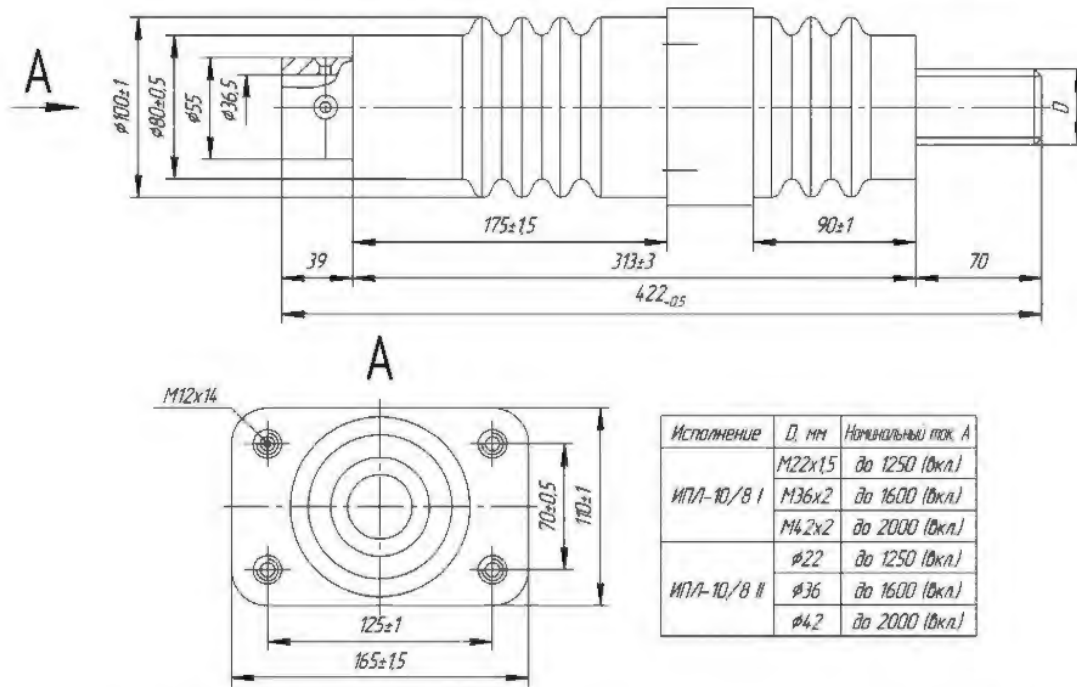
Габаритные и установочные размеры изолятора проходного ИПЛ-10/8 III.
